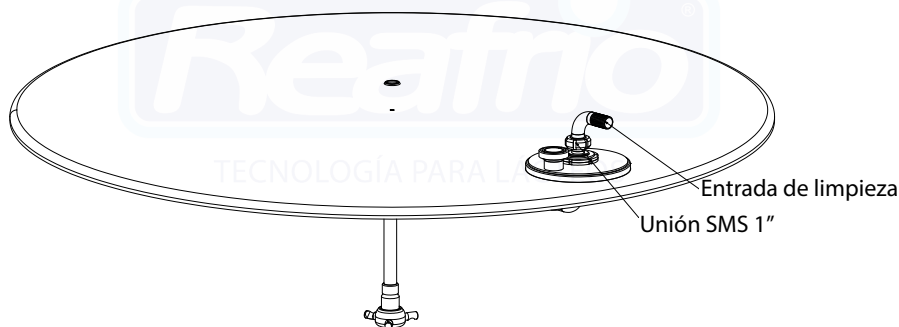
Montaje del Conjunto de Alimentación del Spray
